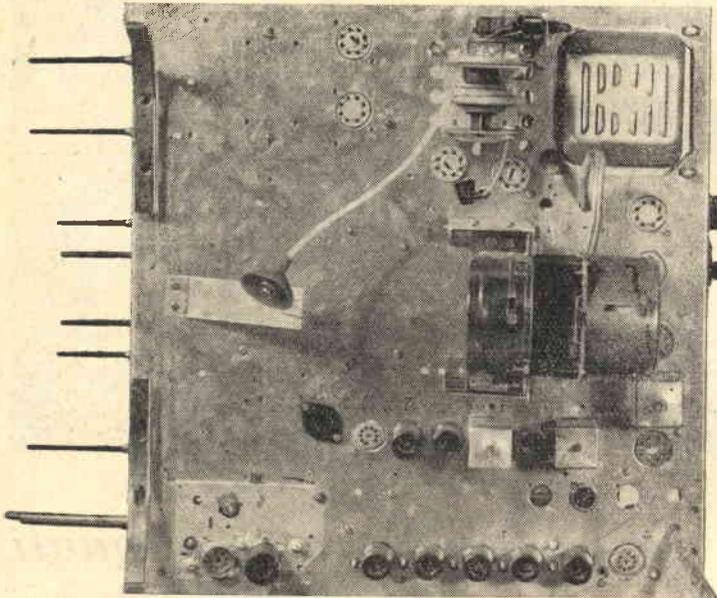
Come si presenta il telaio a montaggio eseguito di tutti i componenti premontati e meccanici.
